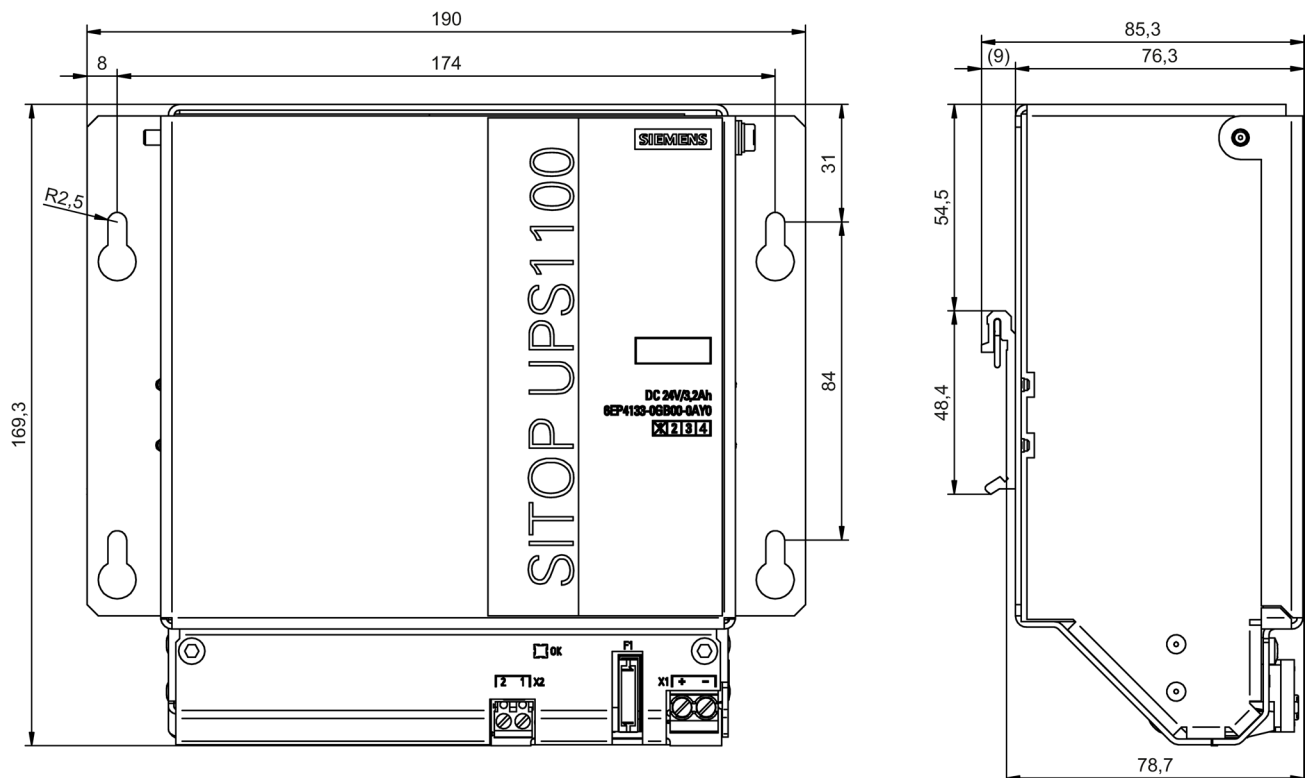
Maßzeichnung 6EP4133-0GB00-0AY0
